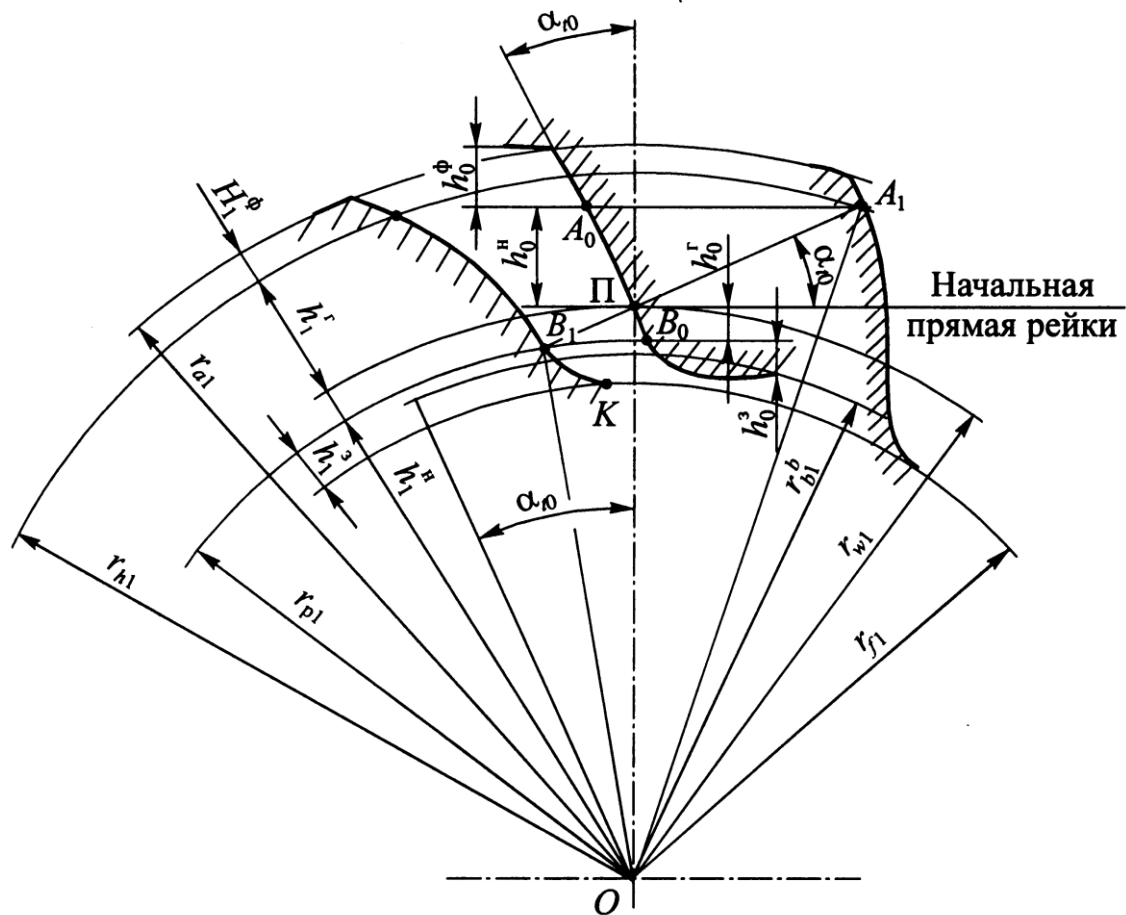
Схема зацепления инструментальной рейки с эвольвентным колесом
